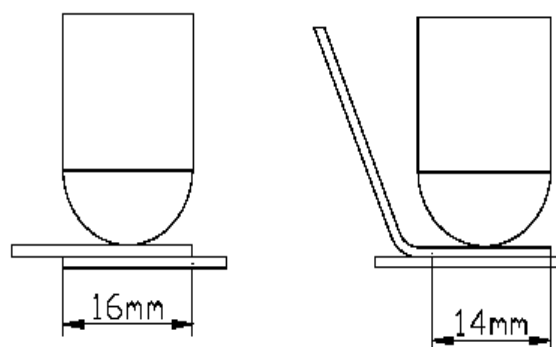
Juntas Traslapadas Tipo 1 y 2.
